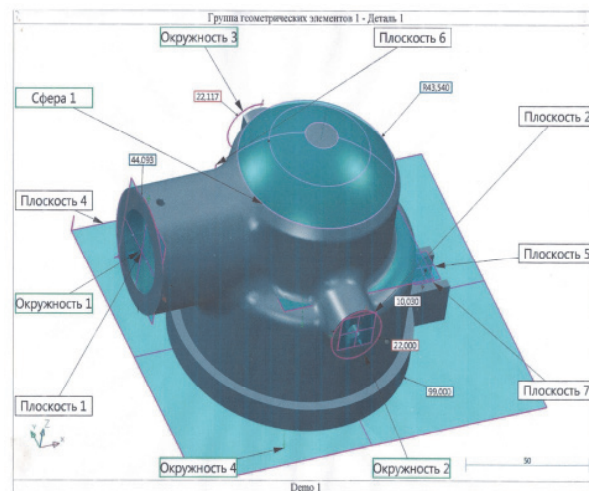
Трехмерная модель корпусной детали (обозначены основные и вспомогательные конструкторские базы)
